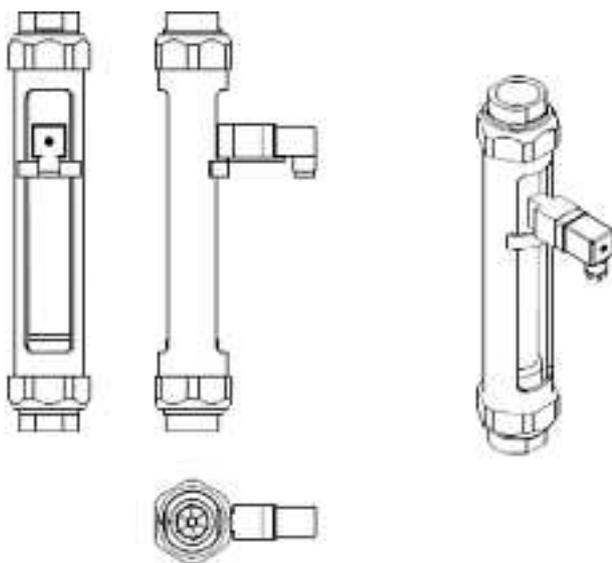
Fissaggio contatto K17 a FVA Tubux M30
